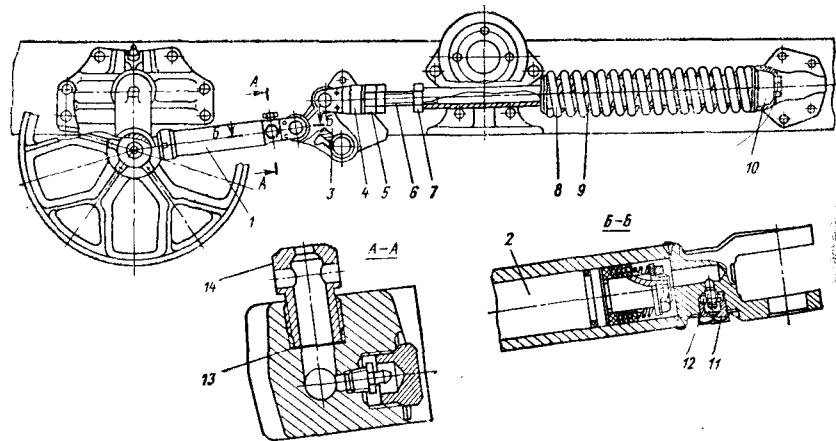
Кривошипное натяжное приспособление трактора Т-150:
